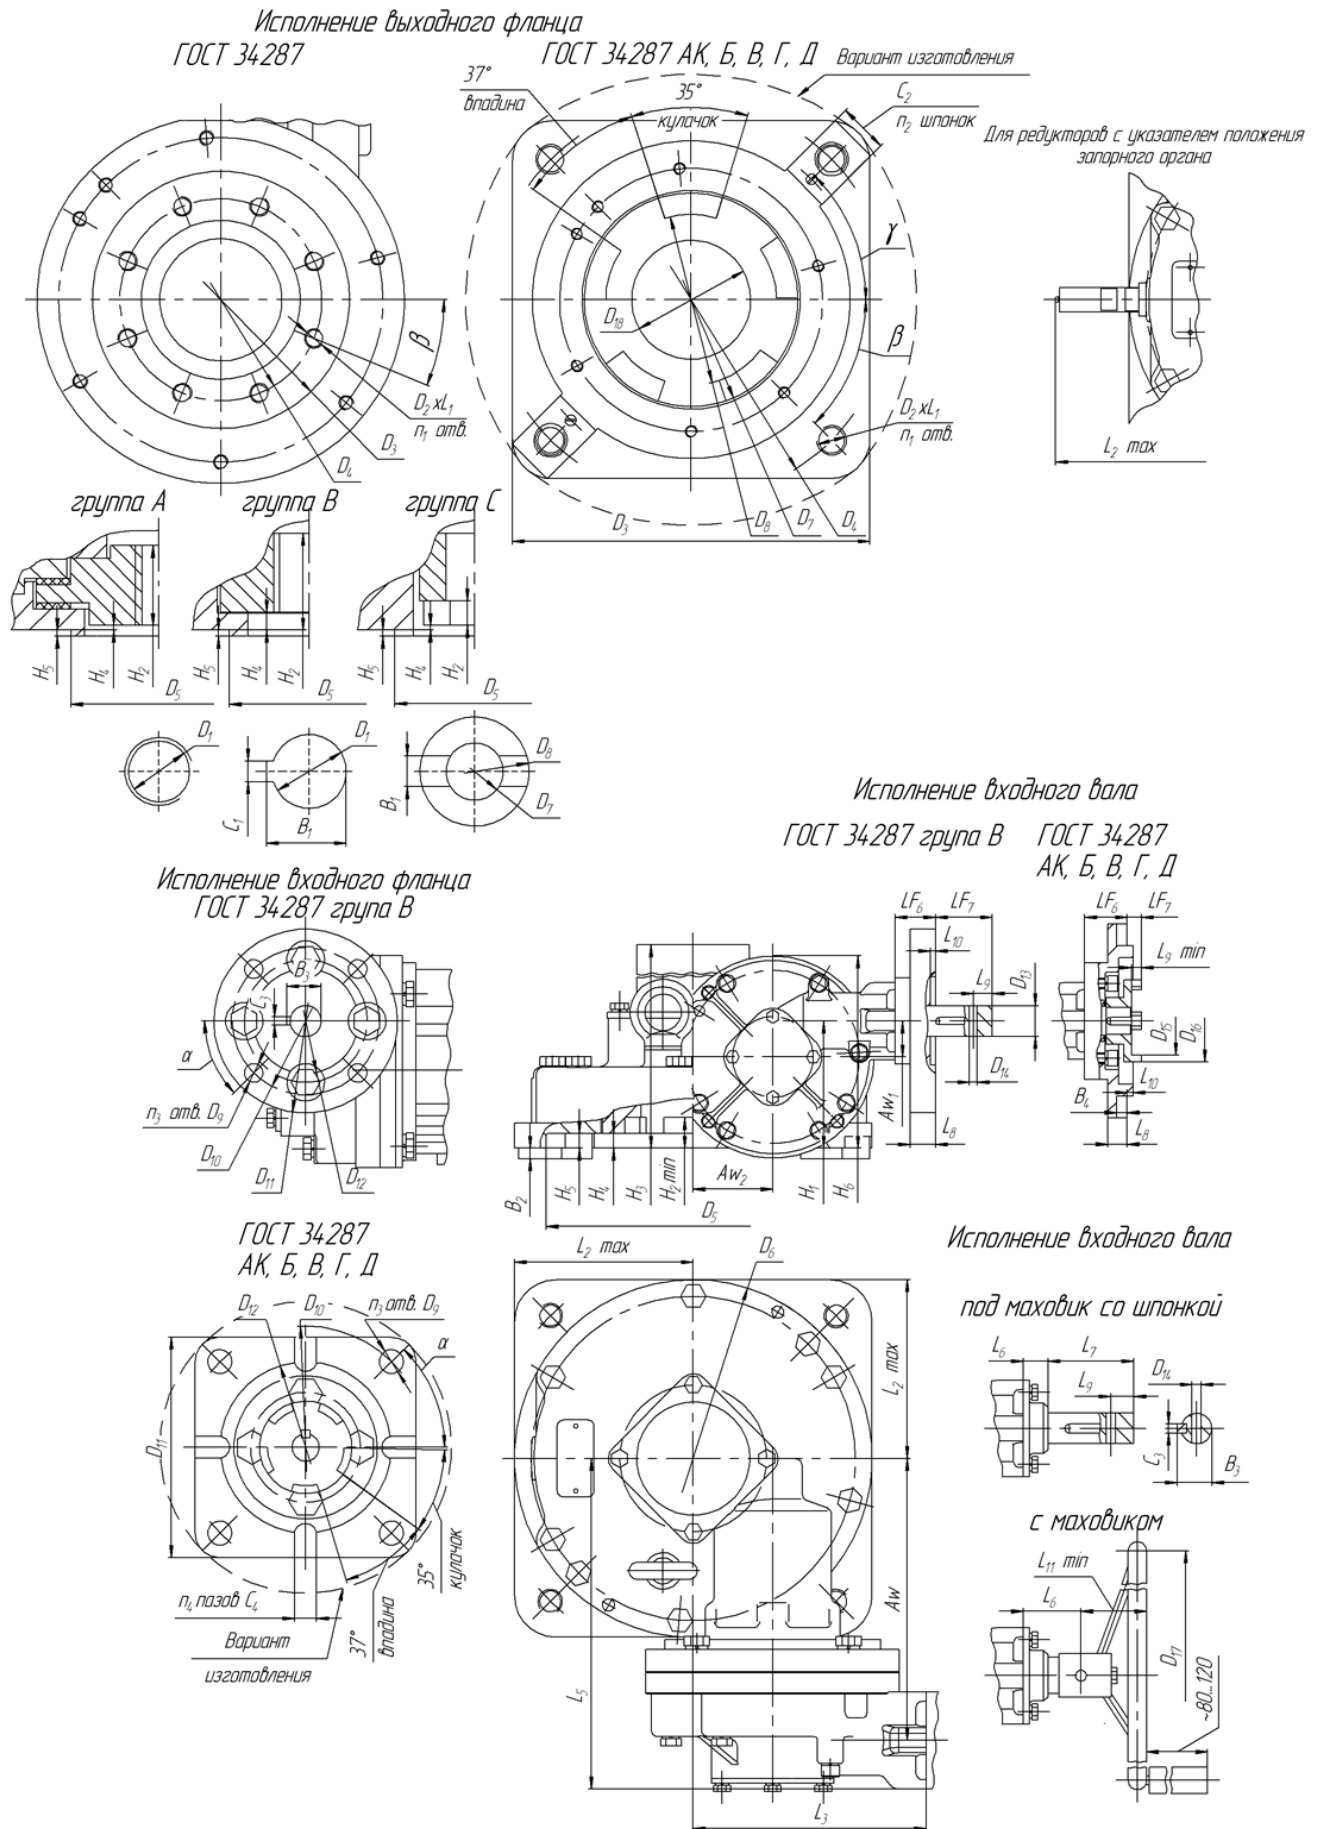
Габаритные и присоединительные размеры выходных вала и фланца редукторов РЗАМ-С2
